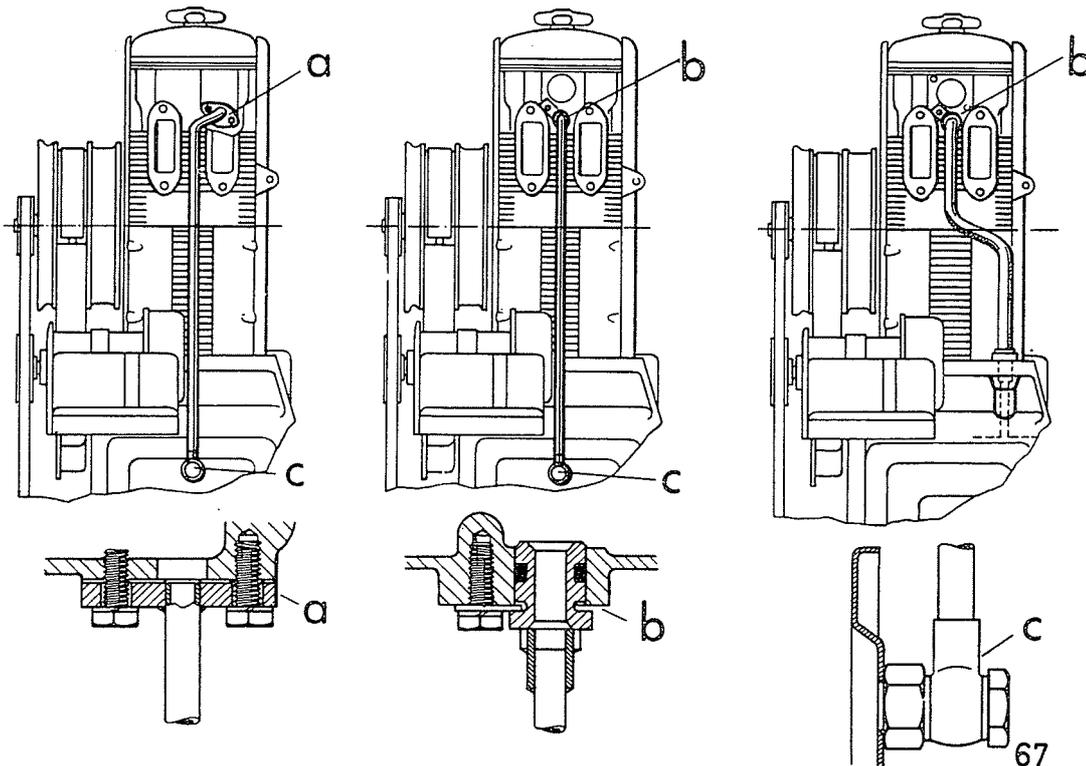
Ausführungen des Ölrücklaufrohres am Motor F/A 1L 514
